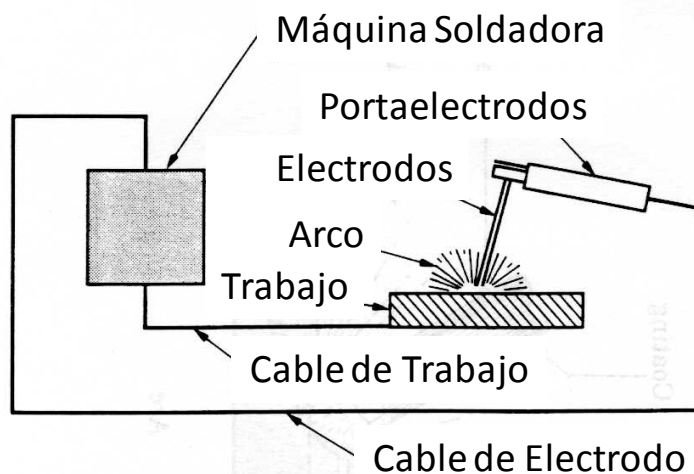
Elementos que componen el circuito en la soldadura por arco eléctrico.
